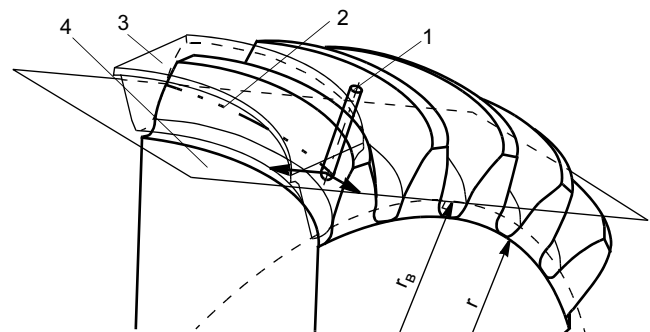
Станочное зацепление пальцевой фрезы с арочным зубом
